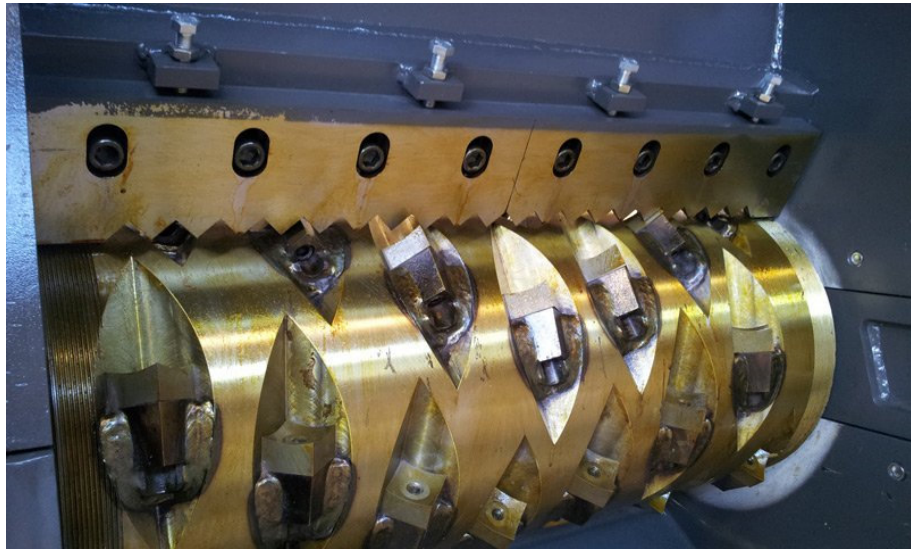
Vorderansicht oberes Statormesser mit Einstellschrauben
